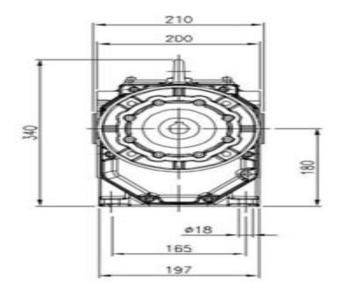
REDUCTEUR DIMENSION 210 MM
